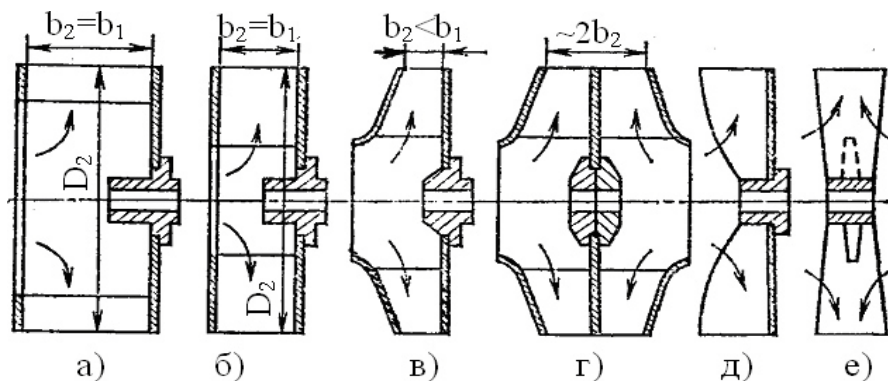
Схемы конструкций рабочих колес центробежных вентиляторов
